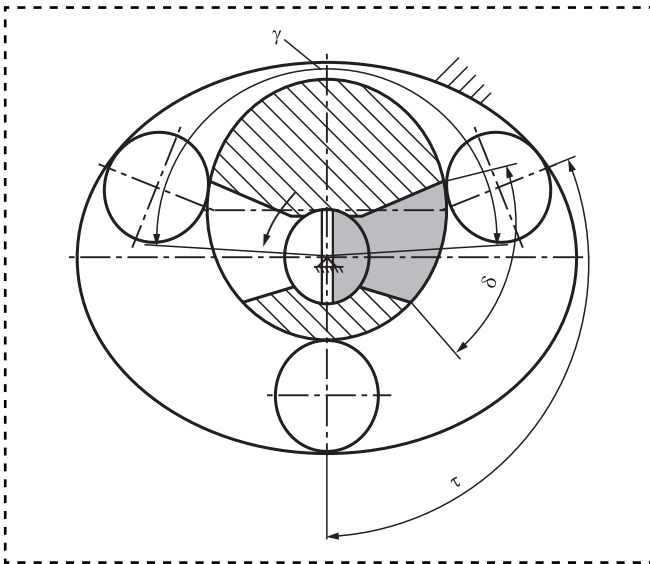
ПРМ схемы 2-1 с каналами в цилиндрической части солнечной шестерни [6]
